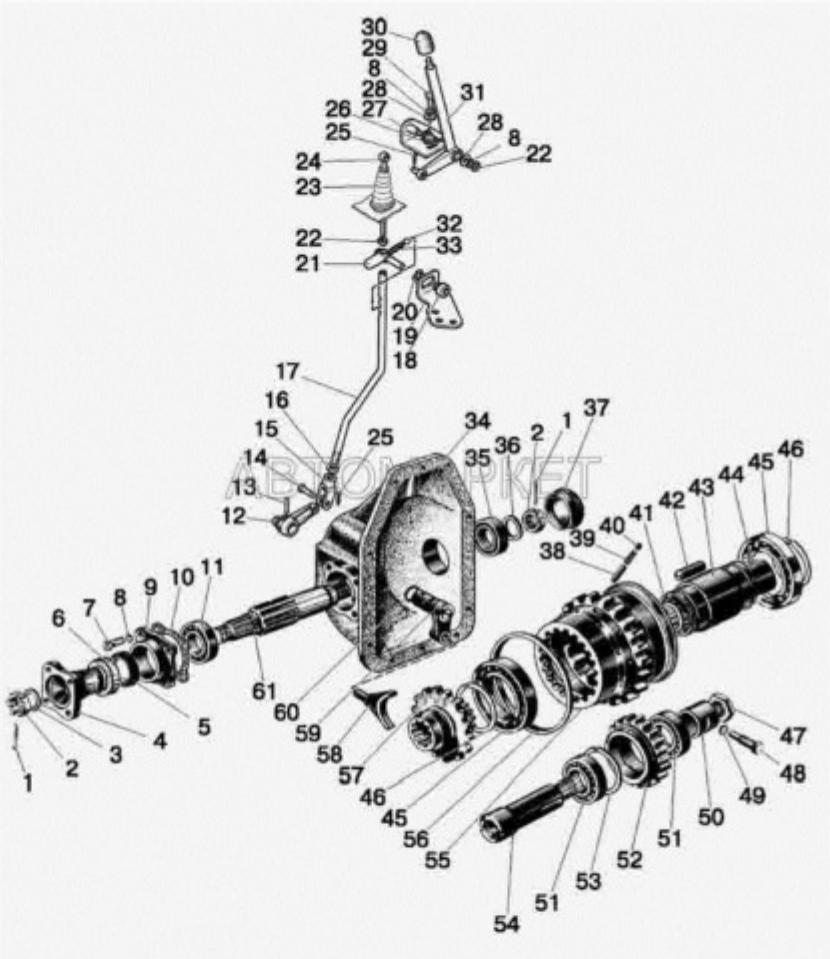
Раздаточная коробка трактора МТЗ-82.
